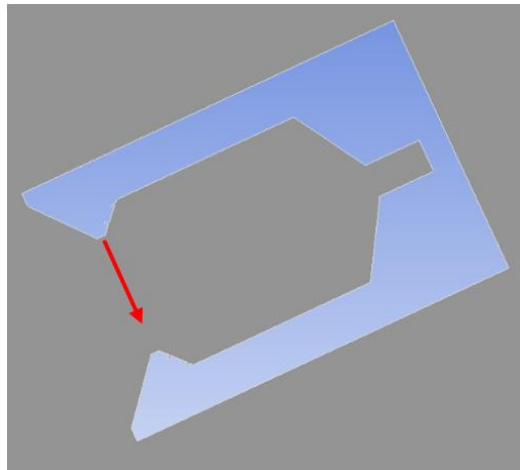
Rappresentazione della variante 1, la freccia in rosso indica la posizione da cui fuoriesce il getto d'aria
